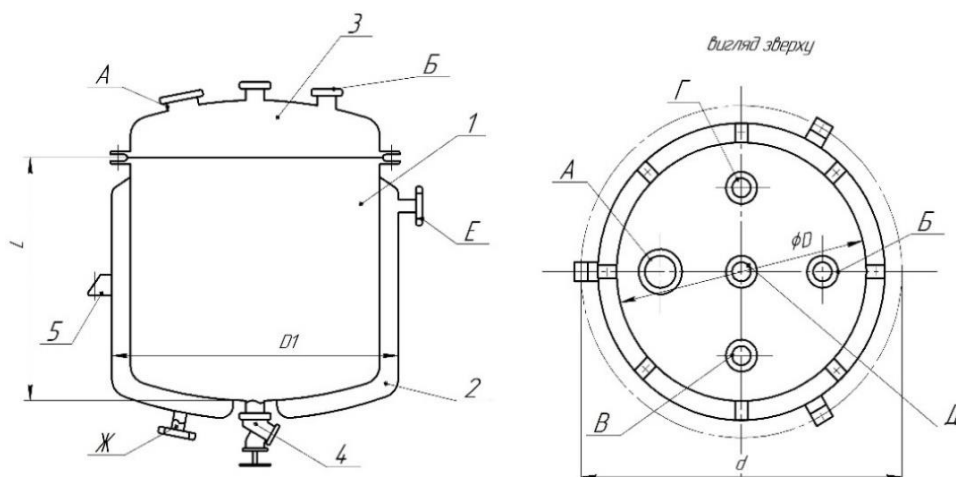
Конструкція концентратора розчину сульфатної кислоти: 1 – корпус; 2- сорочка; 3-кришка; 4 - зливний кран; 5 - опорні лапи;.
